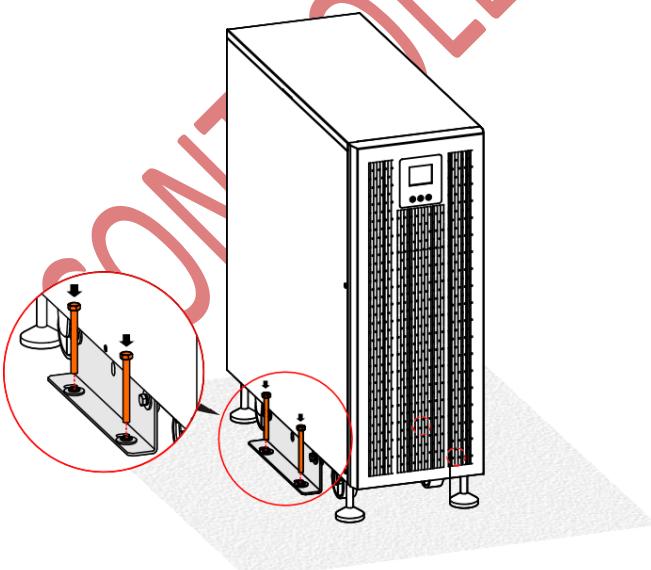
Ekspansi baut struktur Dan instalasi
